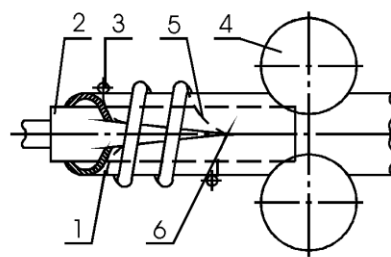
Схема высокочастотной сварки с индукционным подводом тока: 1 — трубная заготовка; 2 — ферритовый стержень; 3 — индуктор; 4 — сжимающие валки; 5 — путь тока; 6 — точка схождения кромок
